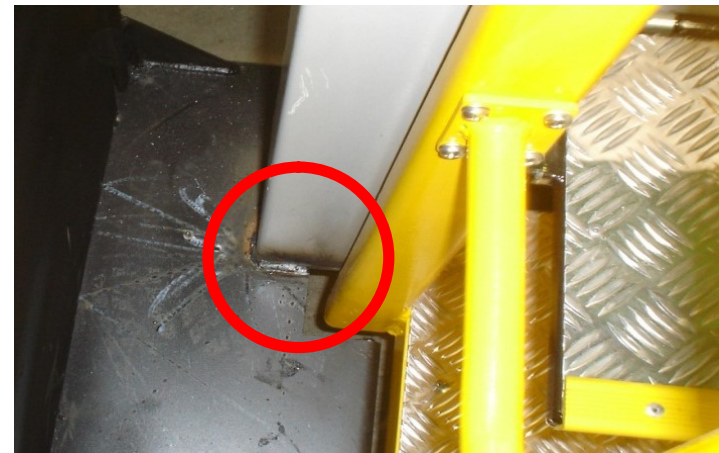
Indicação do ponto onde deverá ser efetuada a solda.
